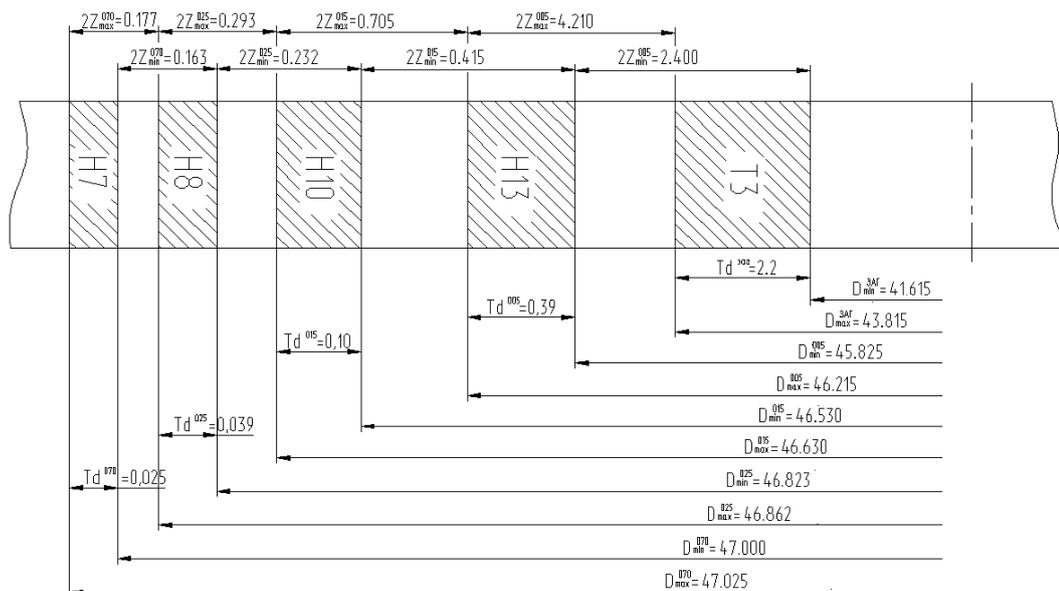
Схема расположения припусков, допусков и операционных
